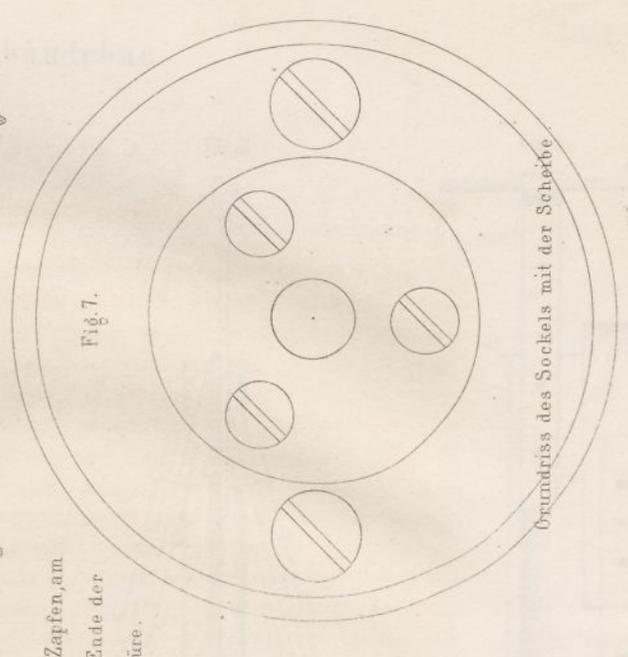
Grundriss des Sockels mit der Scherbe.
